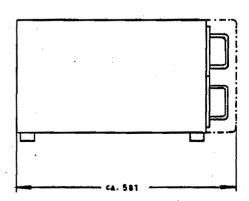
Abmessungen in mm des gemeinsamen Gerätekastens
